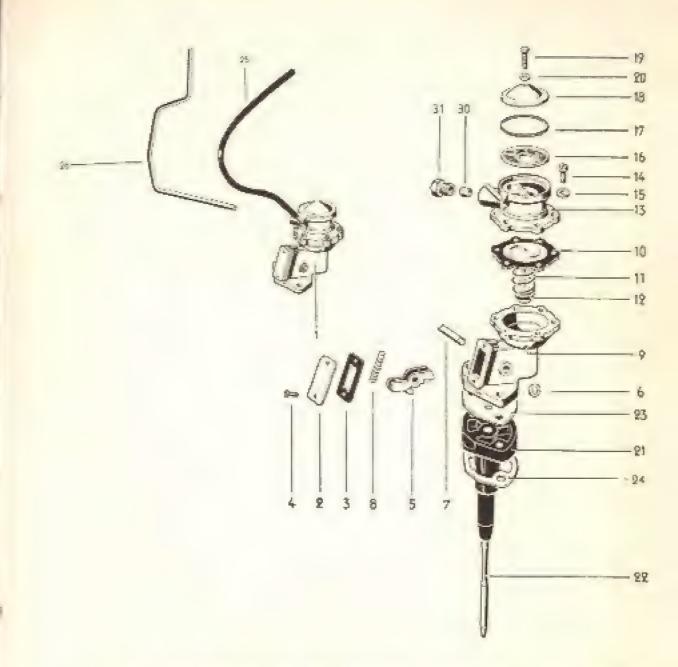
E — Bomba de gasolina dos motores "1 500" e "1 600". Como se vê, é semelhante a do motor "1 300". As diferenças se encontram na parte superior. A nomenclatura das peças é idéntica, com as excessões seguintes: 16 — filtro de tela; 17 — juntas do filtro; 18 — tampa superior; 30 — cone de vedação; 31 — porca de conexão. A bomba de gasolina do motor plano "1 600" é idéntica a do motor "1 300", com a única diferença de ter o tubo de entrada voltado para a frente do motor.
